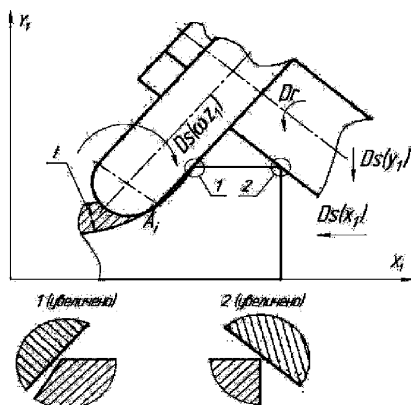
Схема до визначення умови неврізання ланок інструментального блоку в необроблювані ділянки заготовки
